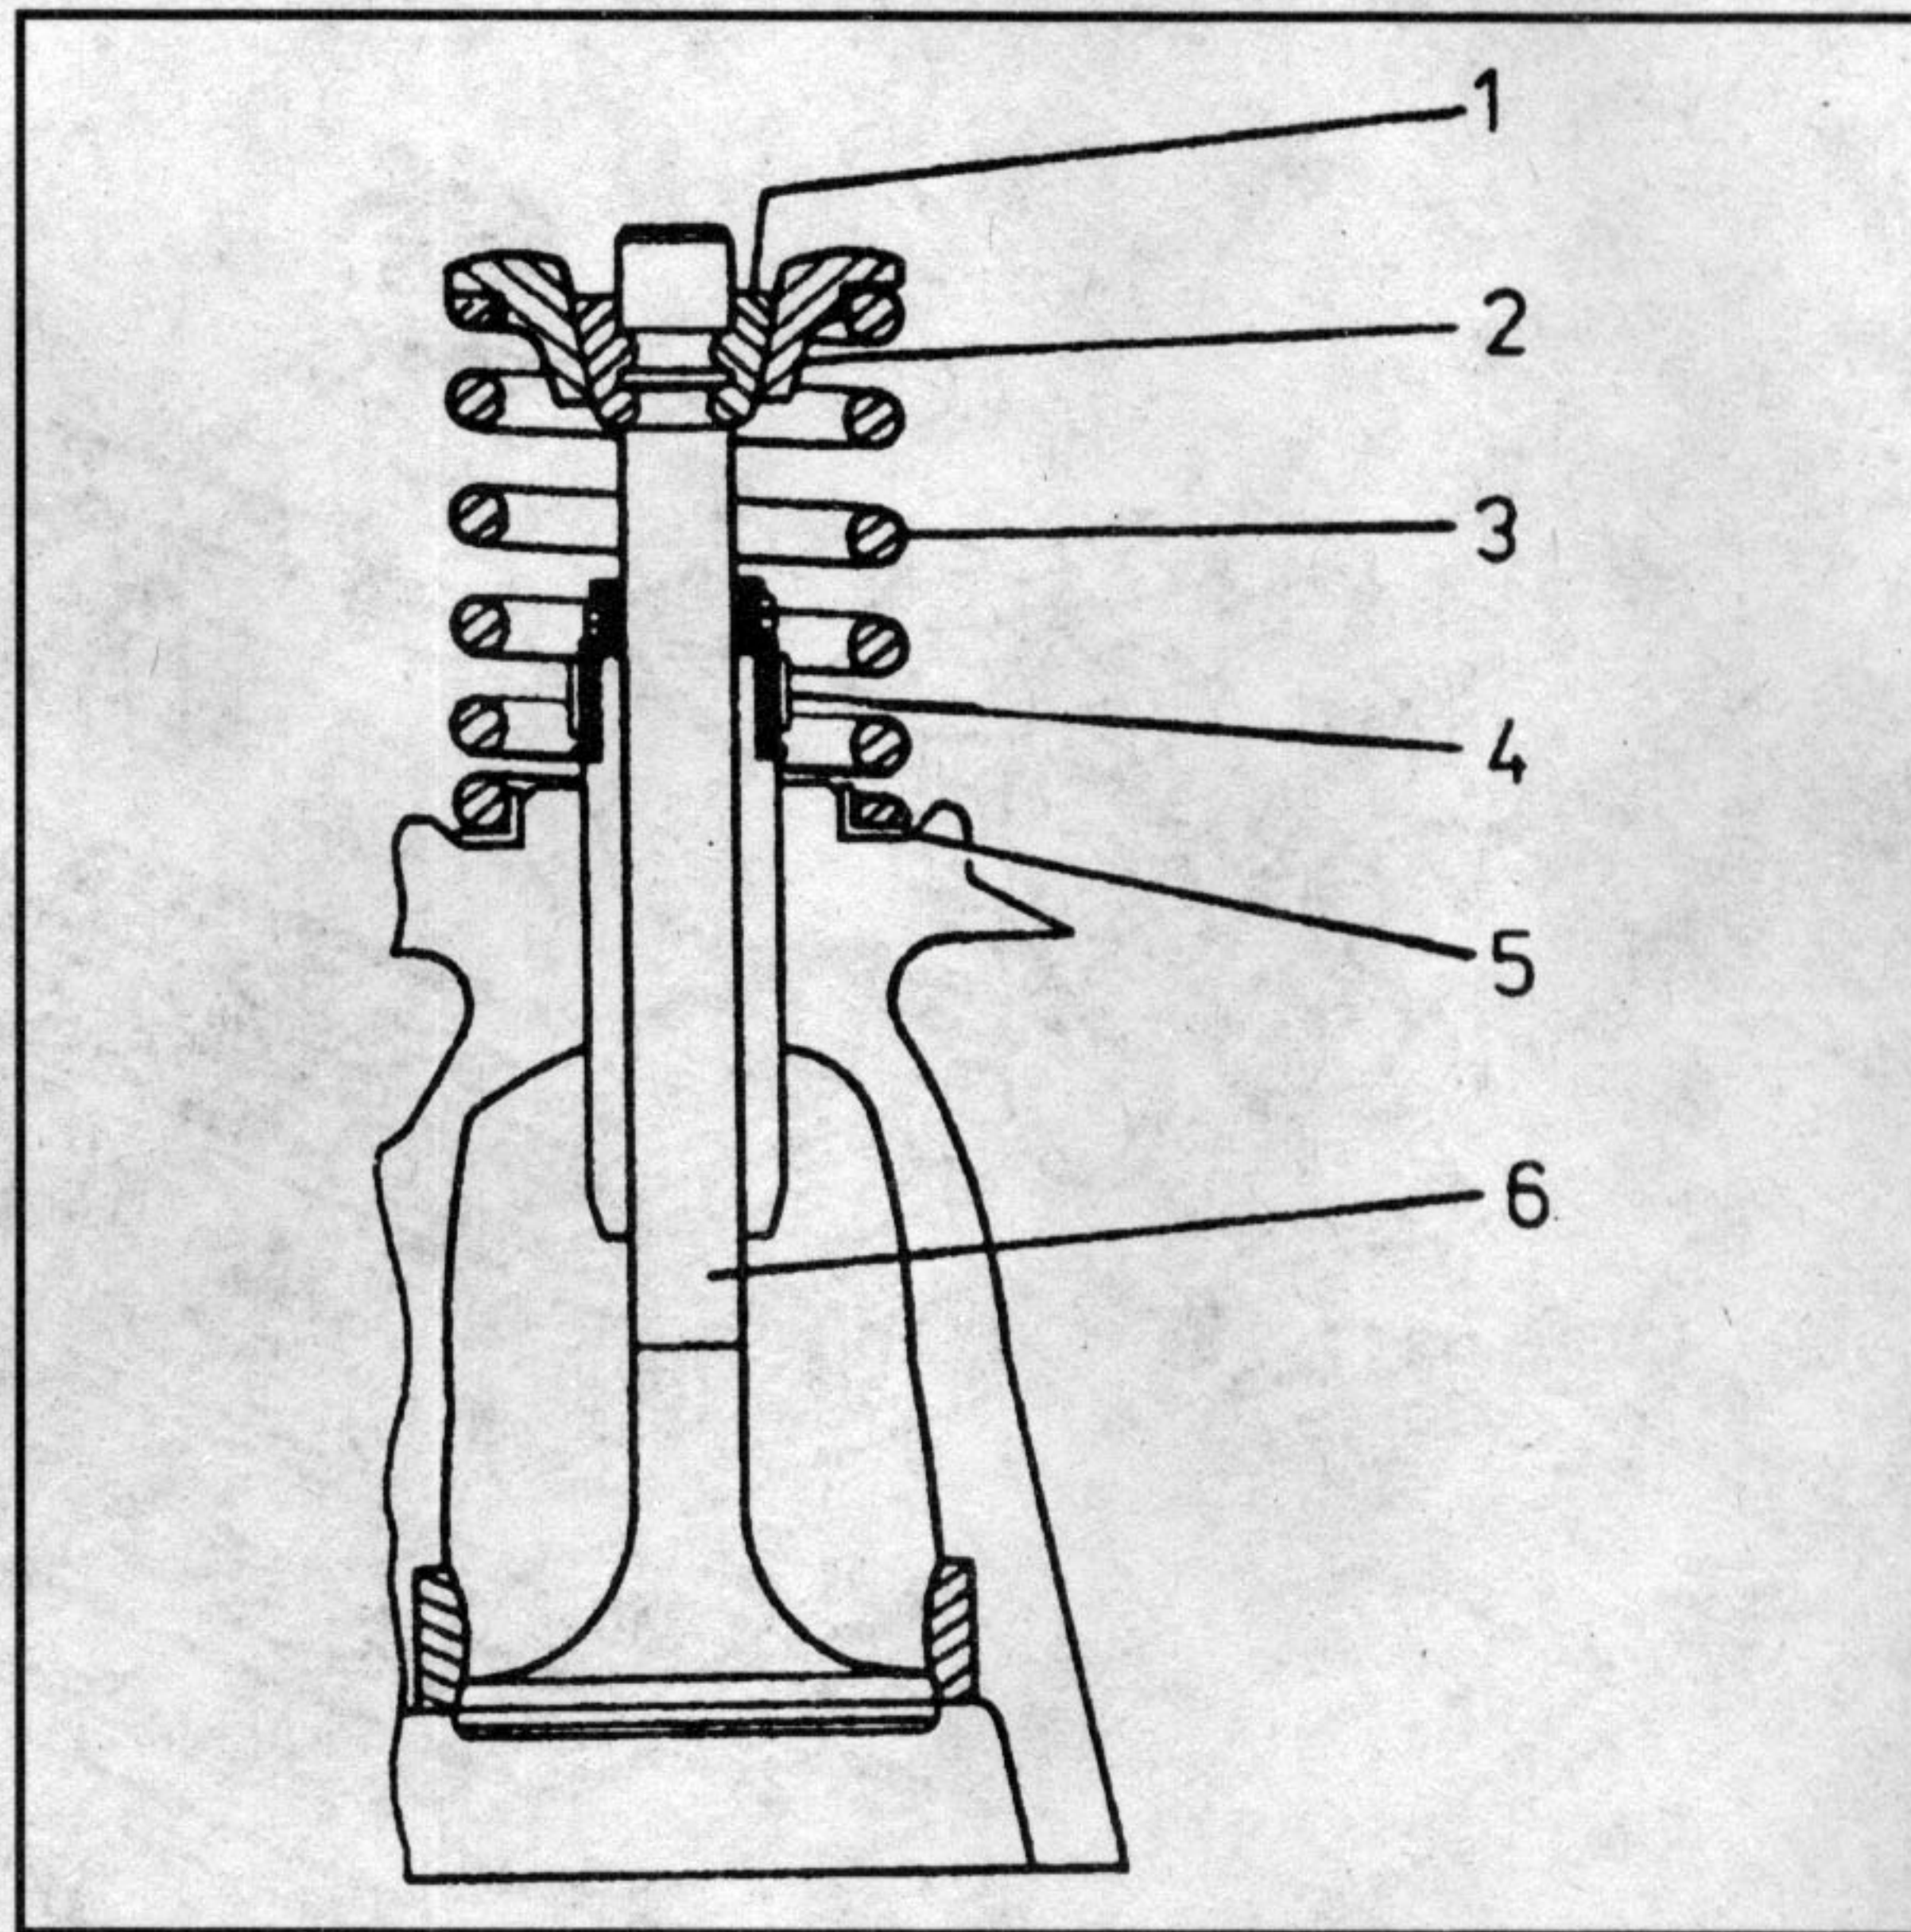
Клапан в сборе в головке блока двигателя В13/В14 — расположение маслоотражательного колпачка
